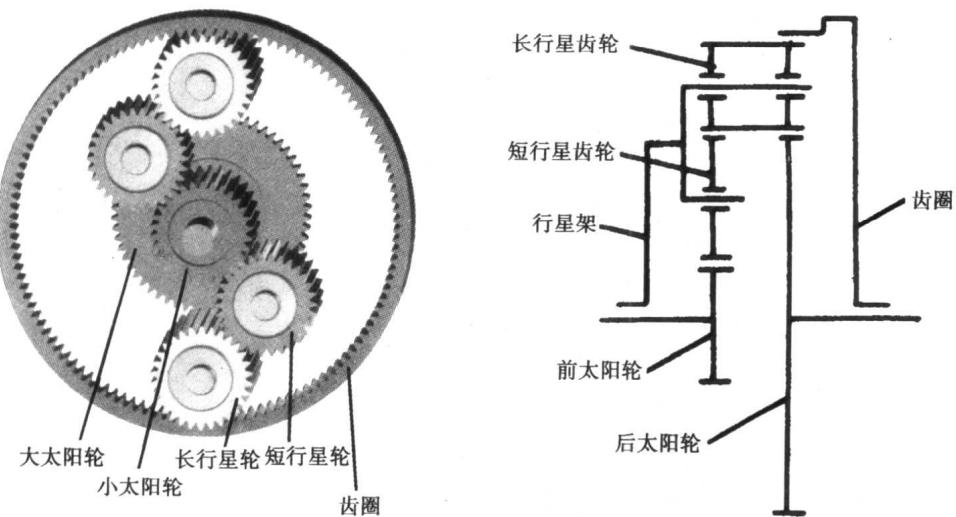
拉维奈尔赫式行星齿轮机构示意图
